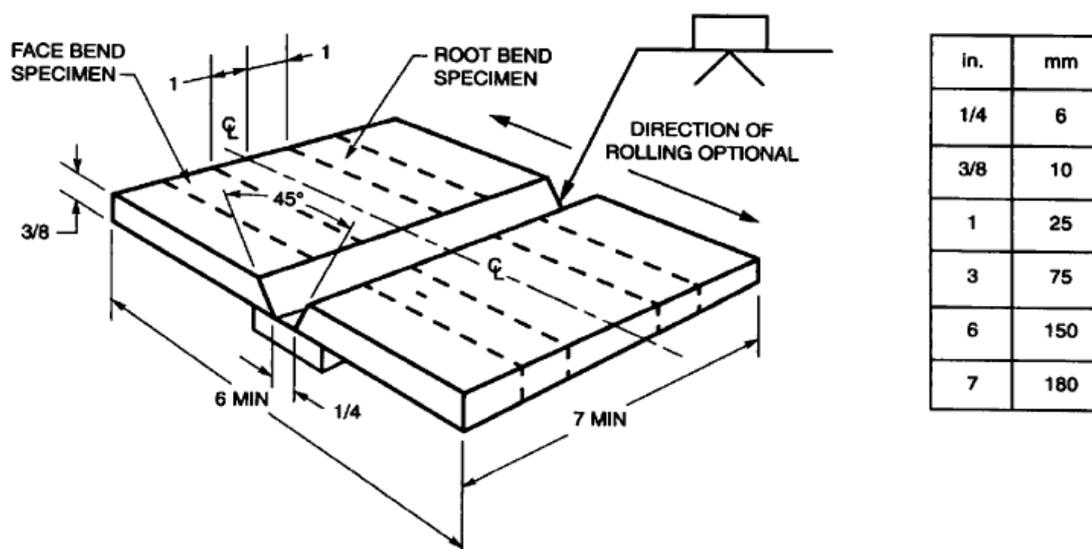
Placa de prueba para calificación de soldador.
